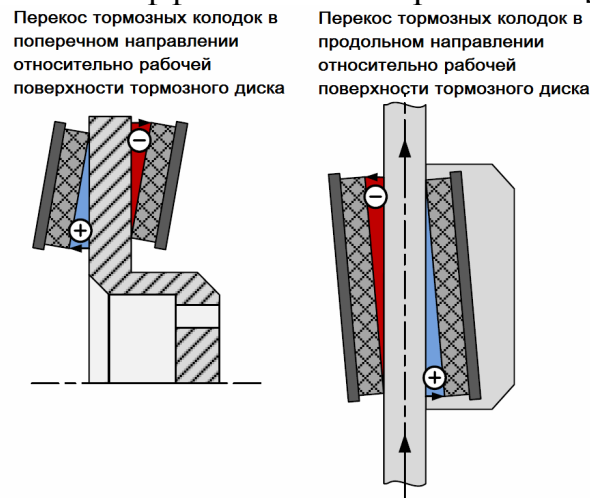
Неравномерный износ рабочей поверхности тормозного диска
